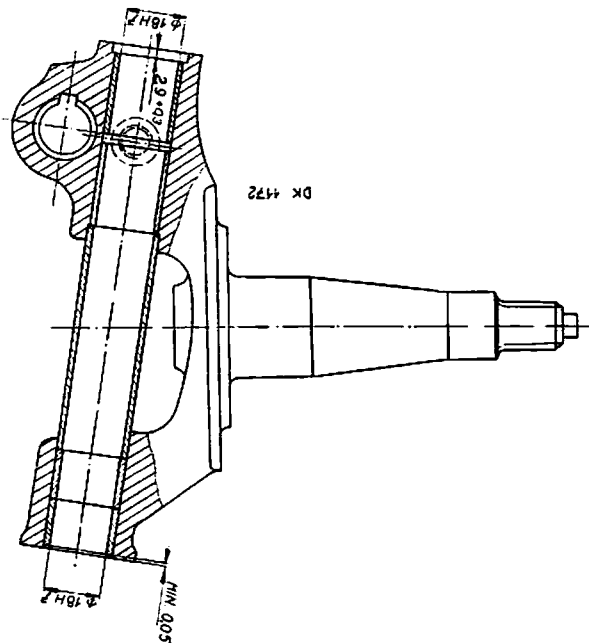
/6/2 Achsschenkel – Abmessungen für das Einpressen und Bearbeiten der Buchsen
